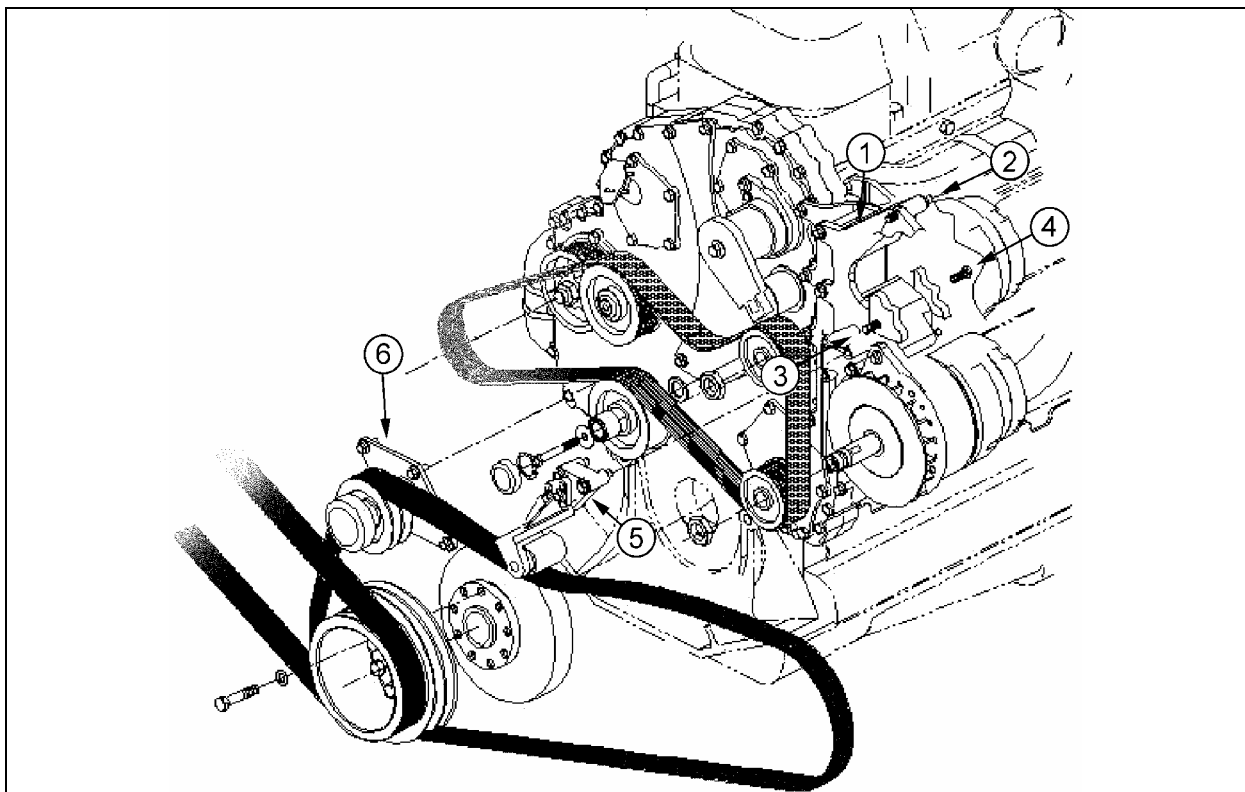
INSTALLATION DES ALTERNATEURS BOSCH, VUE ÉCLATÉE
